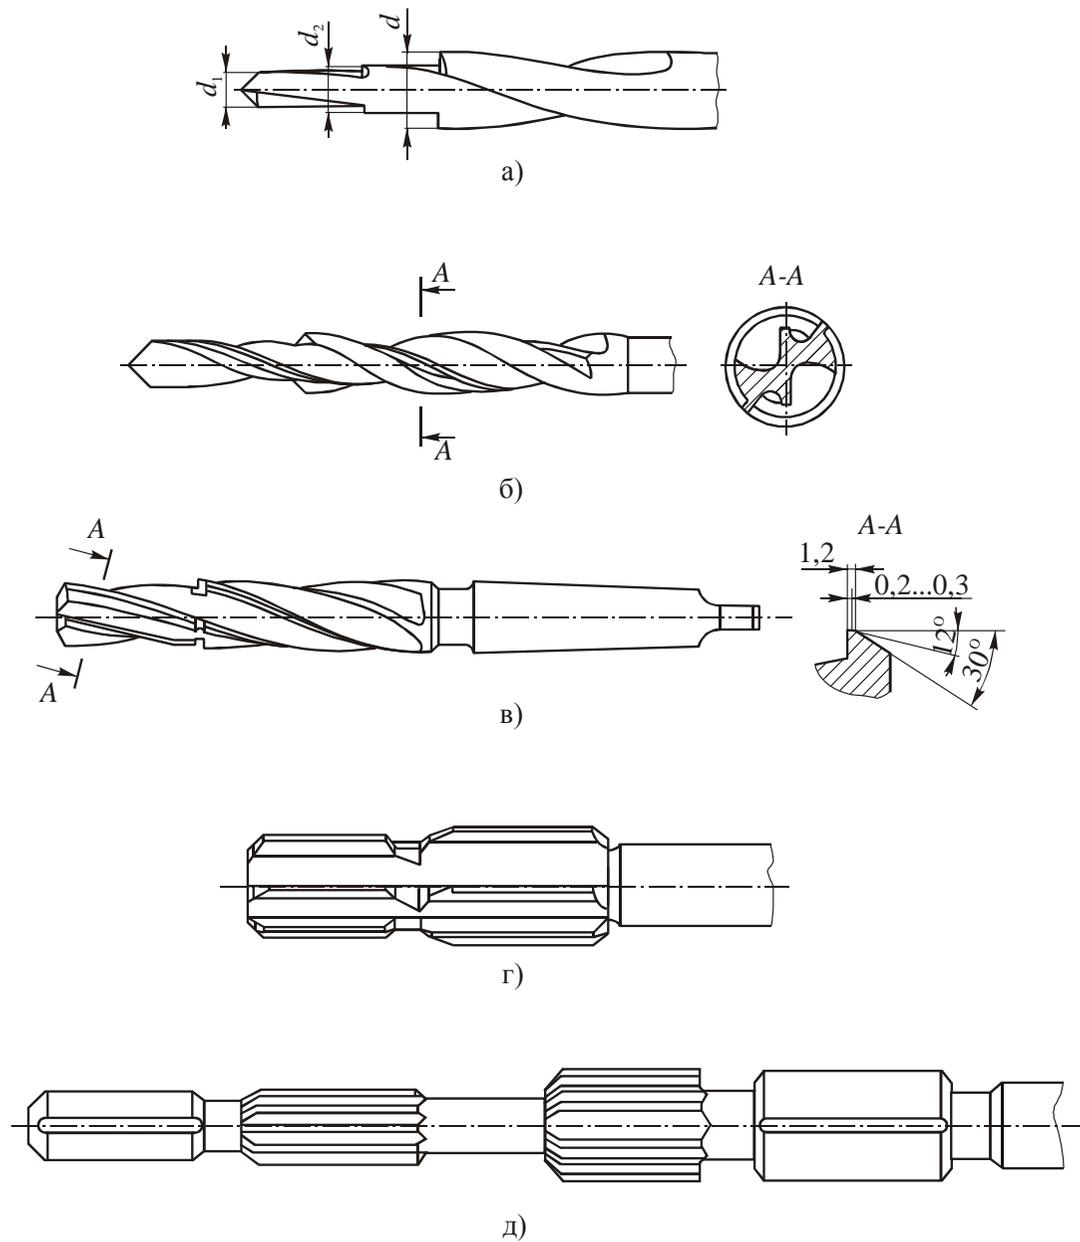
Комбинированные (ступенчатые) инструменты для обработки отверстий: *а, б* – сверла; *в* – зенкер; *г, д* – развертки
